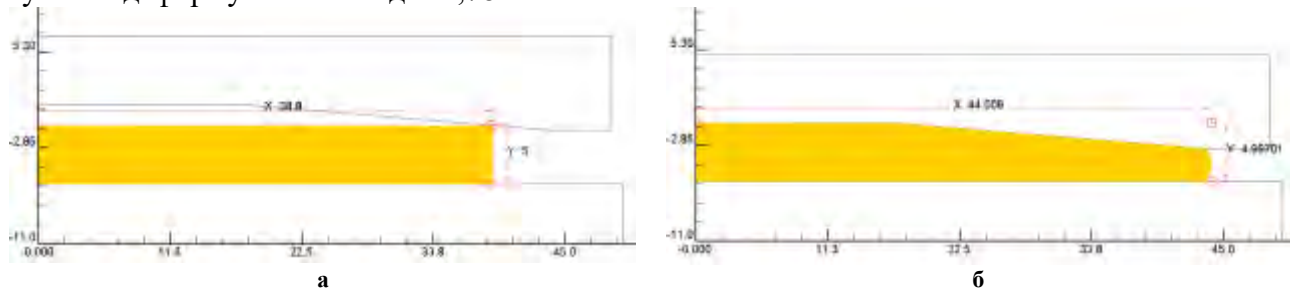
Розрахункова схема процесу гарячого профілювання заготовки:
